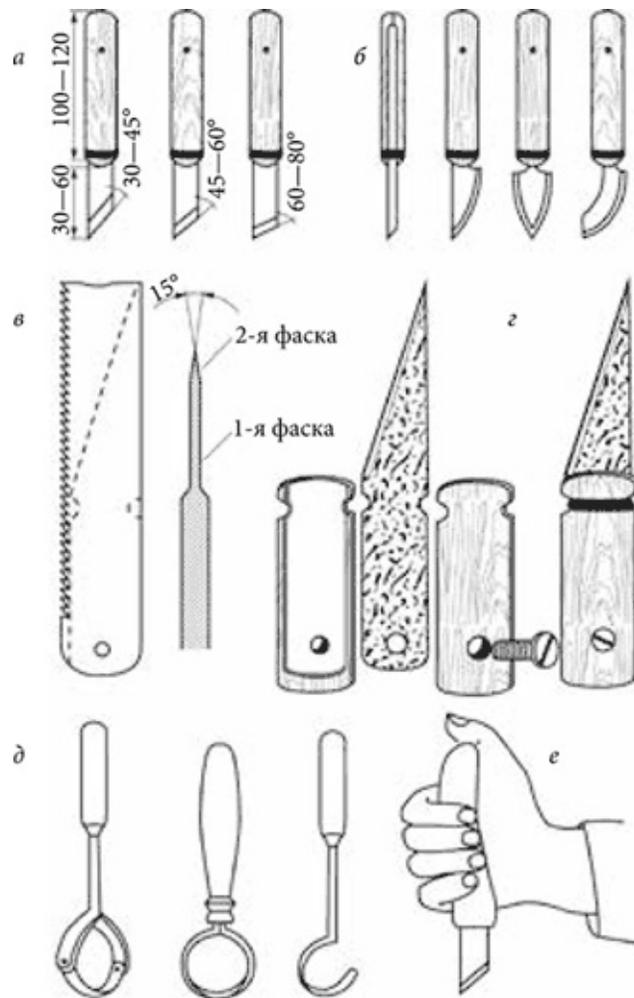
Изготовление ножей из полотна пилы для металла и монтаж их с черенками: а – ножи-косяки с разными углами скоса; б – ножи-резаки; в – линия разреза на большом ножовочном полотне; г – изготовление ручки для большого ножа; д – ложечные ножи; е – захват ножа при резбе.
